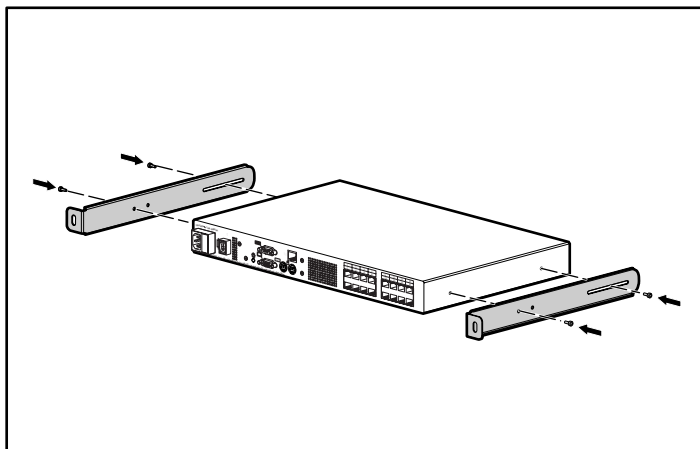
Fissaggio delle staffe per le guide di scorrimento
